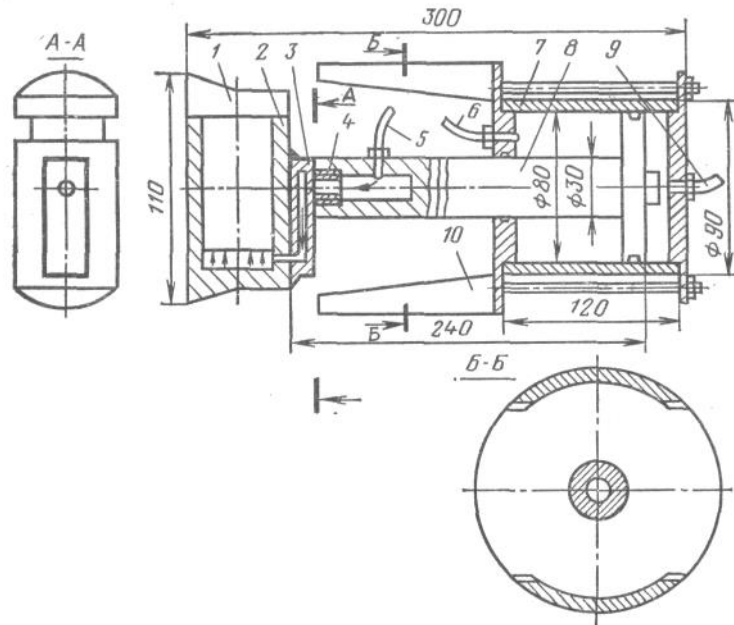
Гідравлічний знімач зовнішнього кільця роликового підшипника ведучої шестерні кінцевої передачі: 1- поршень захоплювач; 2- допоміжний циліндр; 3- призма; 4- штуцер; 5, 6 і 9- патрубки; 7- основний циліндр; 8- шток; 10- упор.
